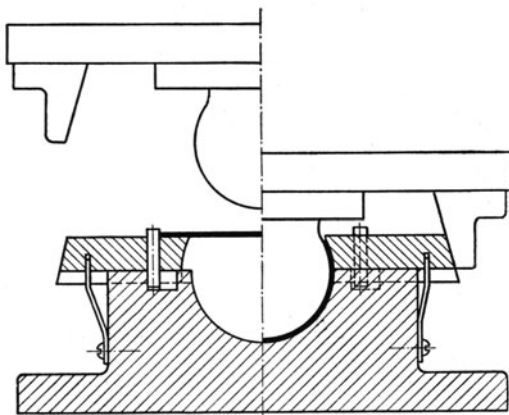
Anbiegewerkzeug mit Seitenschiebern für halbrunde Schalen zum Ausgleich der Rückfederung
